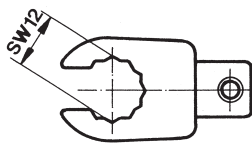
Mauleinsatz SW12 für Montage- und Drehmomentschlüssel Typ 1300A13
